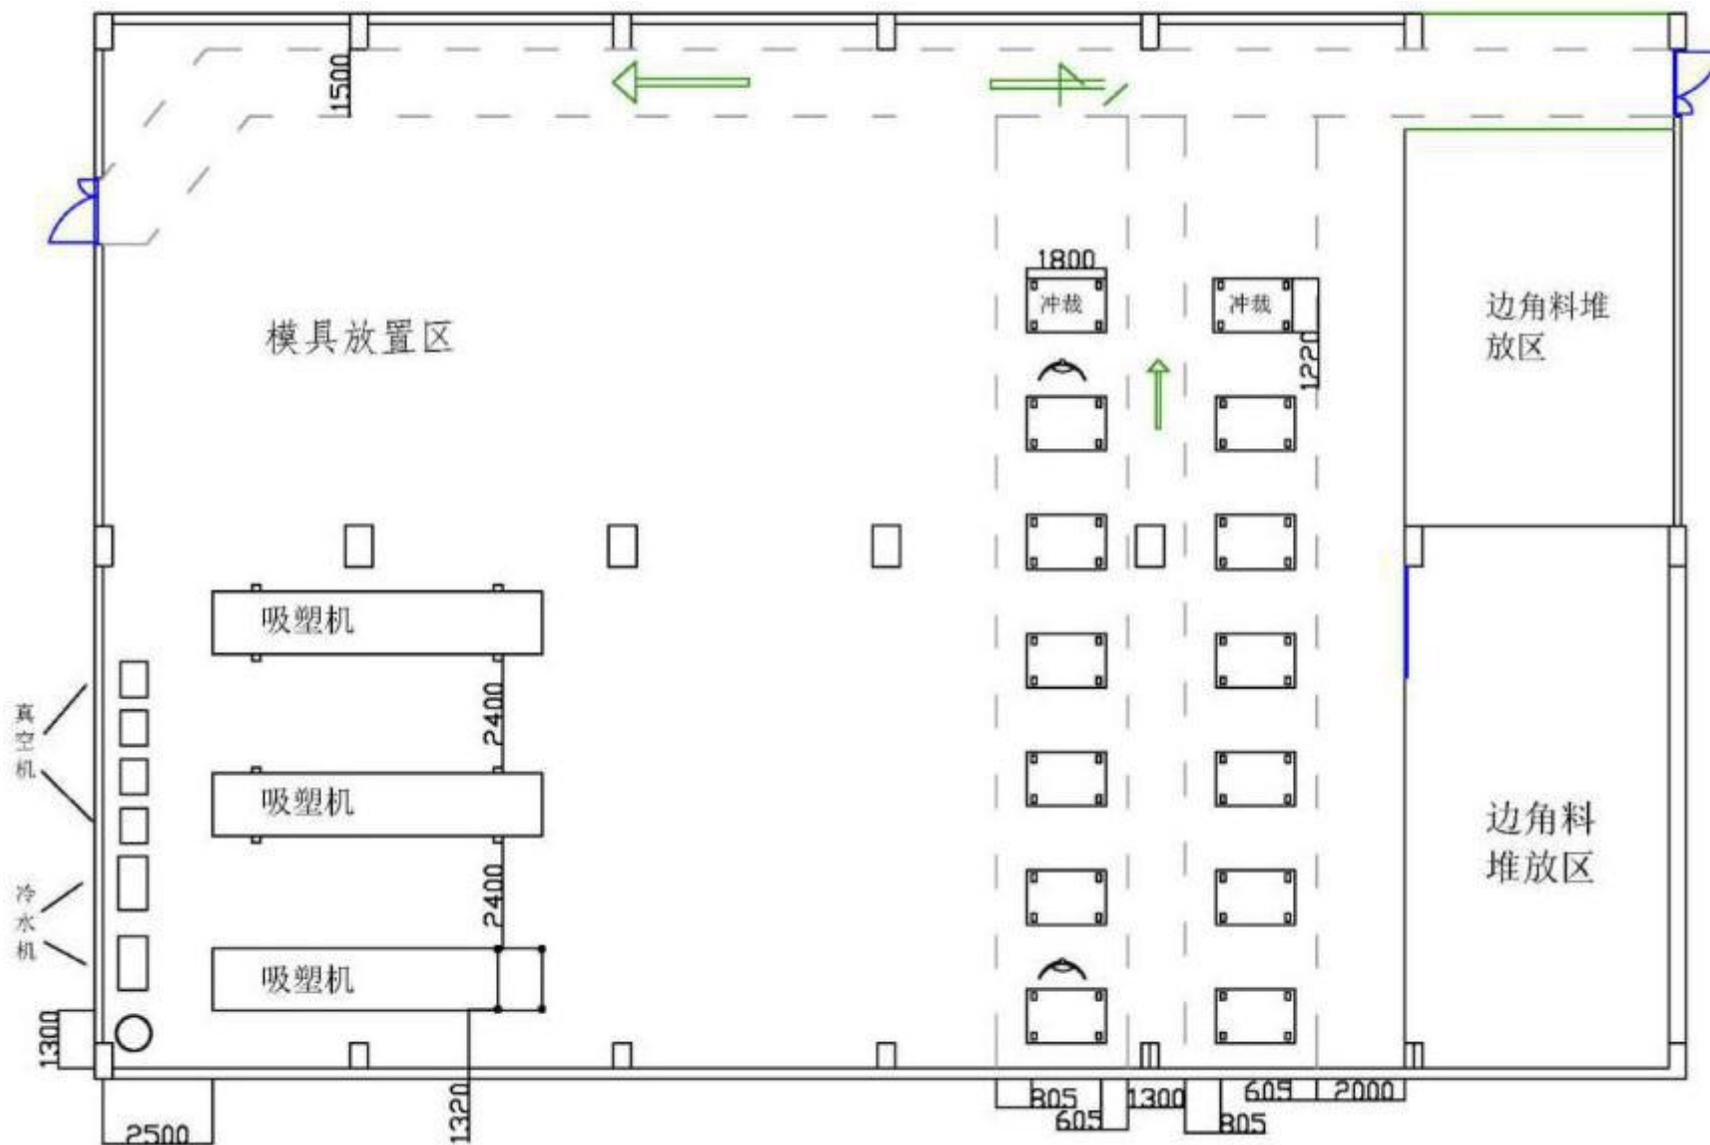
厂房平面布置图（吸塑车间，D 栋二层）
